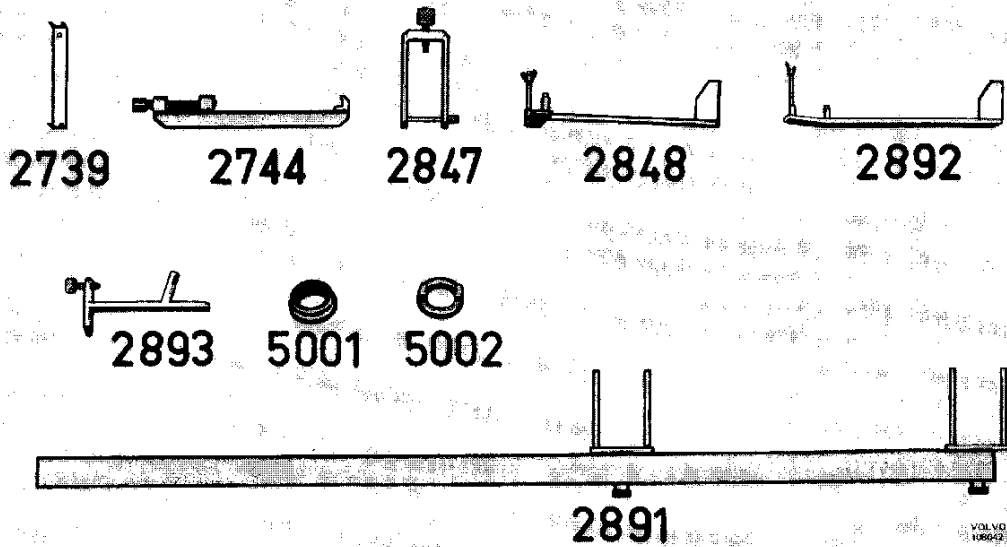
Spezialwerkzeuge für Karosseriereparaturen.
